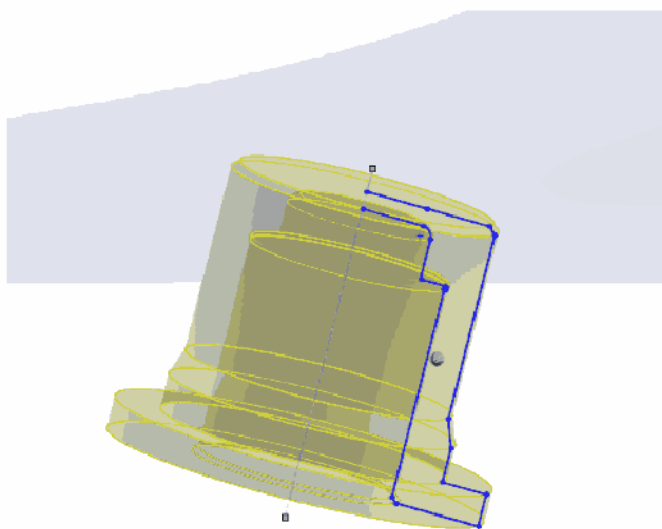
Створення основної частини деталі через «Обертання»
